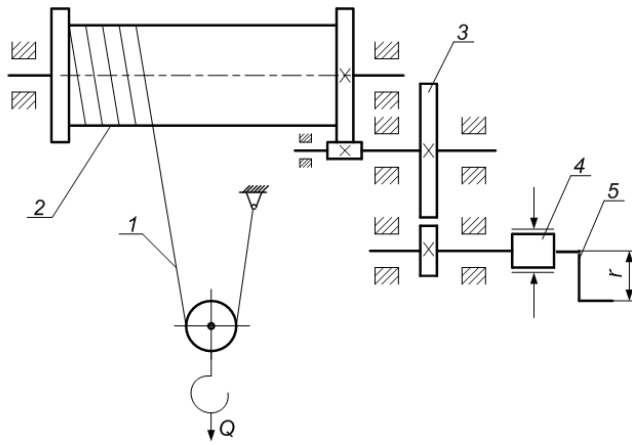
Механізми підйому ВПМ з ручним приводом: 1—гнучкий робочий орган; 2—барабан; 3—передачі; 4—гальмо; 5—приводна рукоятка; 6—вантажозахватний пристрій
